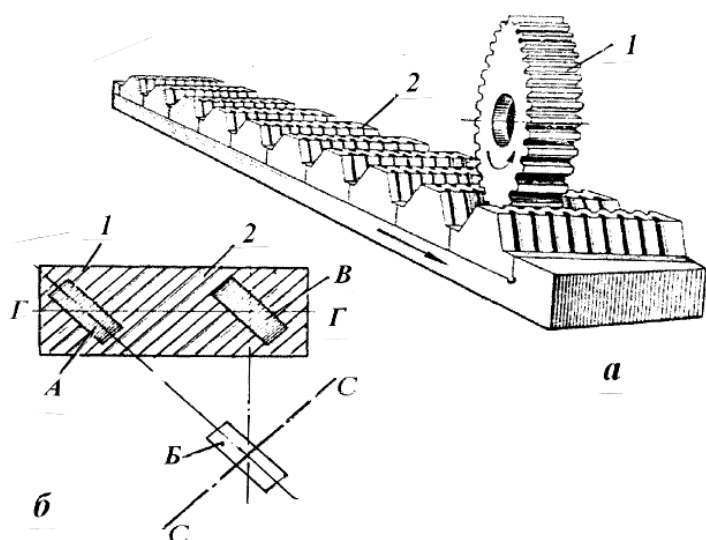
Шевингование шевер-рейкой: а - шевер-рейка; б - схема скольжения шевер-рейки по зубьям зубчатого колеса.
